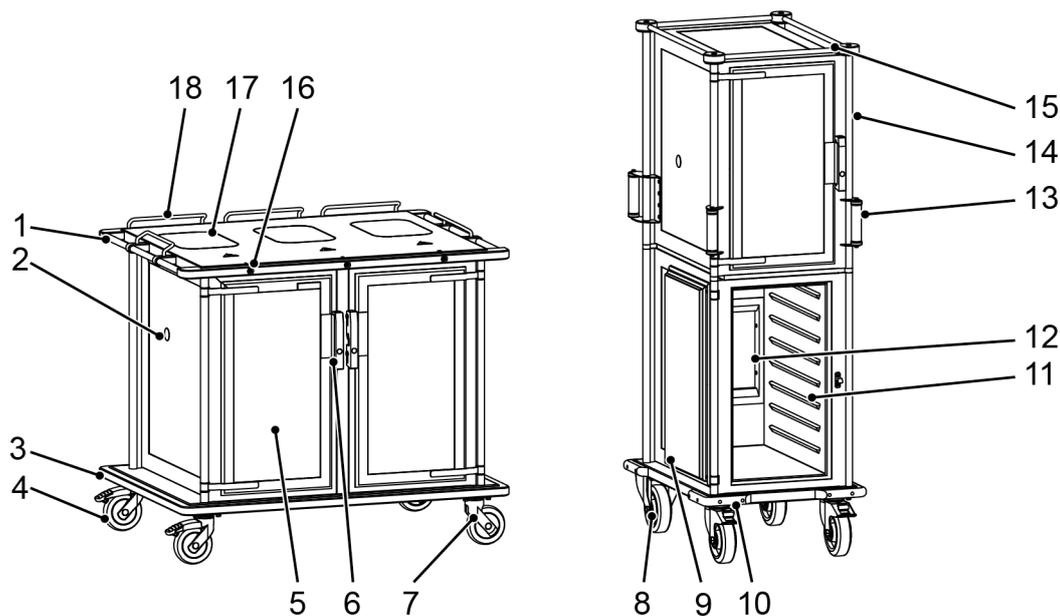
Dimensioni campione di Isobox Mobil Flex
